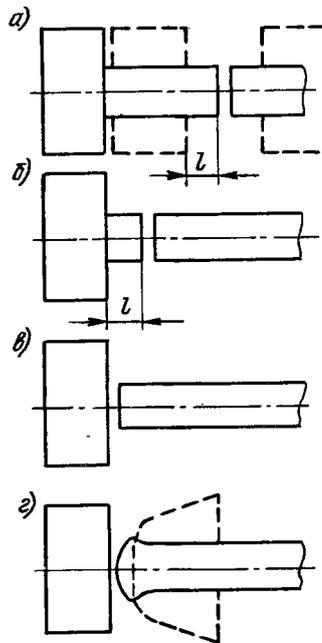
Образцы подготовки разноразмерных деталей к различным способам стыковой сварки
